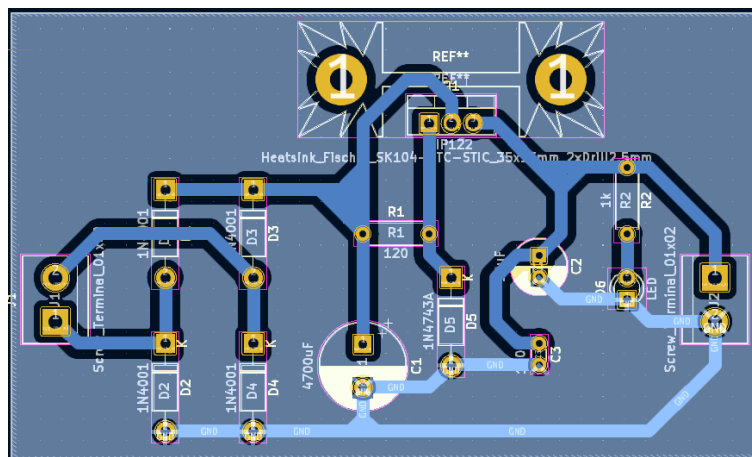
Desenho da placa com plano/malha de terra com as trilhas mais separadas.
